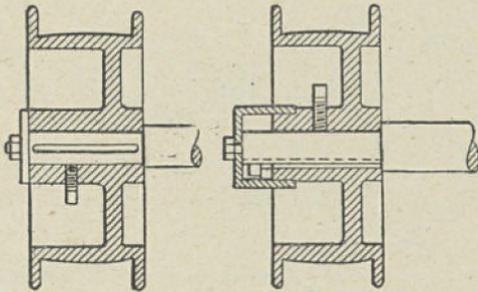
Méthode pour fixer les poulies de régulateur.
